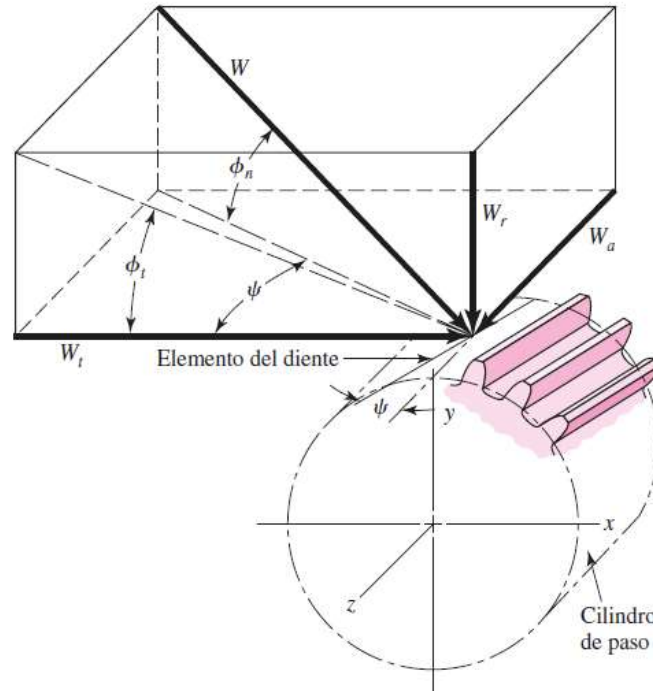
Fuerzas que están actuando en el engranaje helicoidal.
